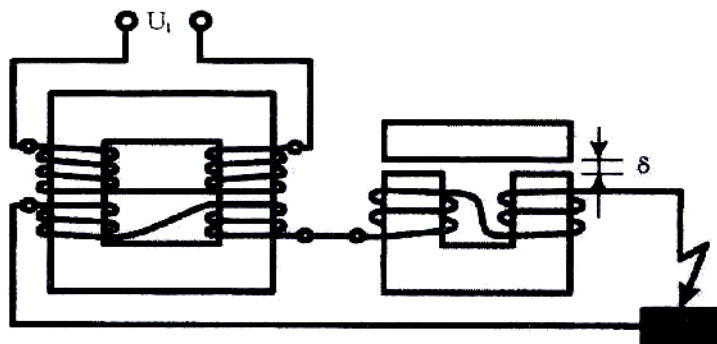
Сварочный трансформатор с реактивной
